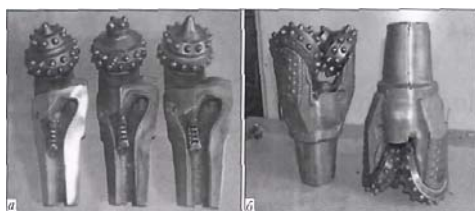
Внешний вид трех элементов долота до сборки и сварки (а) и долота, сваренного электронным пучком (б)
